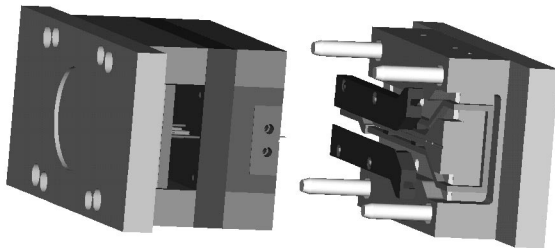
Zeigerwerkzeug mit integriertem Induktor
